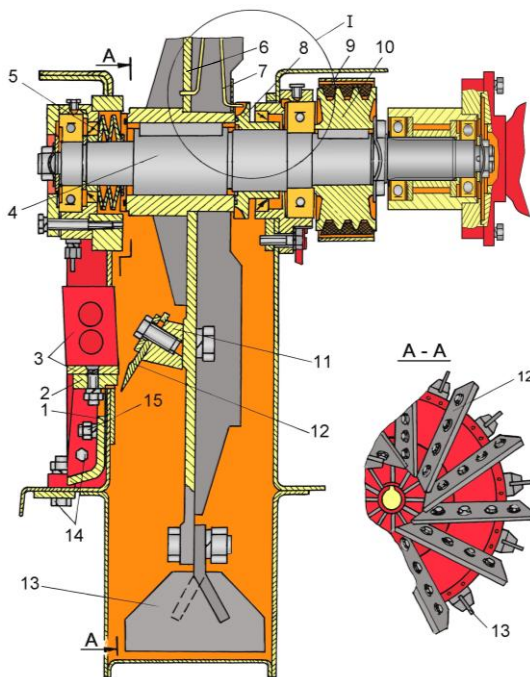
Измельчающий аппарат: 1 – камера; 2 – подбрусник; 3 – противорежущая пластина; 4 – вал; 5 – тарельчатая пружина; 6 – ротор измельчителя; 7 – стопорная пружина; 8 – регулировочная гайка; 9 – ремень; 10 – шкив; 11 – опора ножа; 12 – нож; 13 – лопатки; 14 – регулировочные болты; 15 – болт крепления подбрусника
